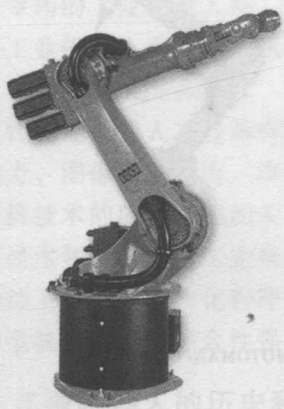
KUKA 焊接机器人 KR 5arc HW
